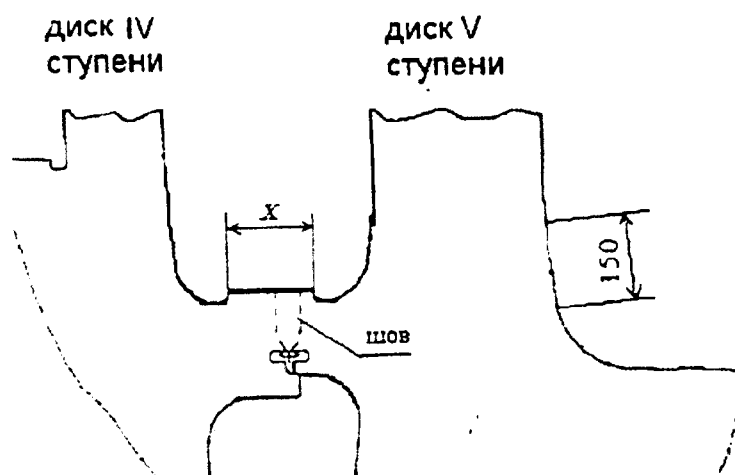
Места зачистки поверхностей ротора под контроль (указаны размерными линиями)
